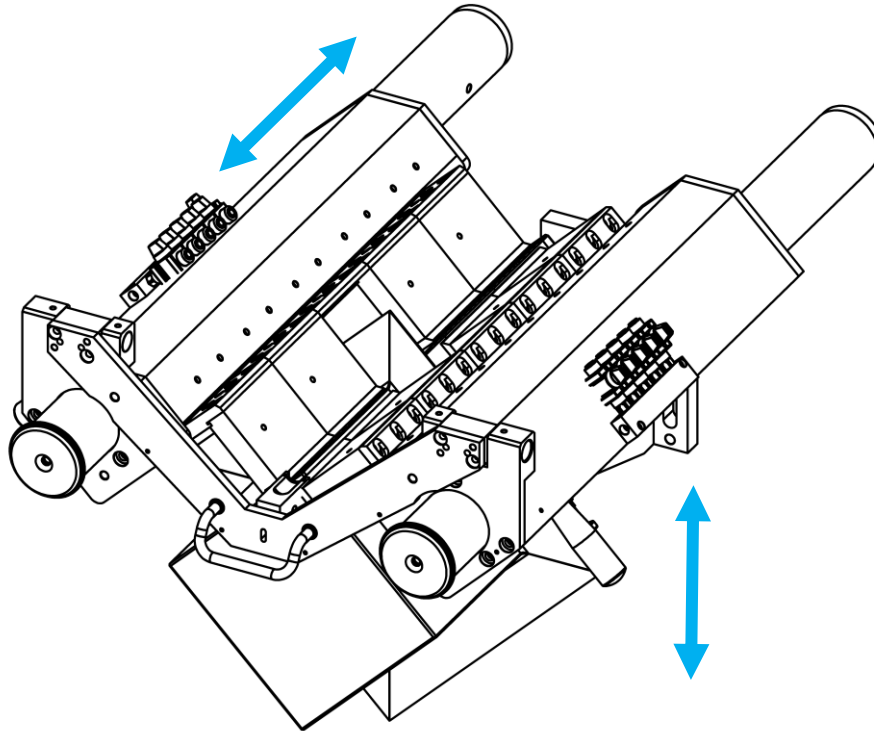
Holmhub und Außenspannsystem zum Einlegen von Bauteilen mit Aufkantung (max. 80 mm) auf gesamte Schweißlänge.
